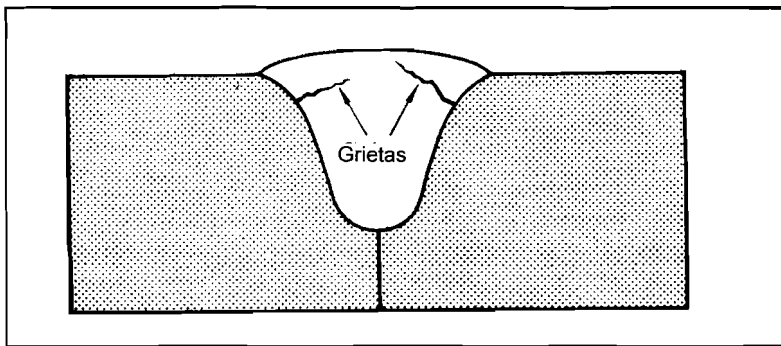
FORMACIÓN DE GRIETAS EN EL CORDÓN DE SOLDADURA DEBIDO A LA BAJA VELOCIDAD DE SOLDEO Y LA ALTA TENSION
